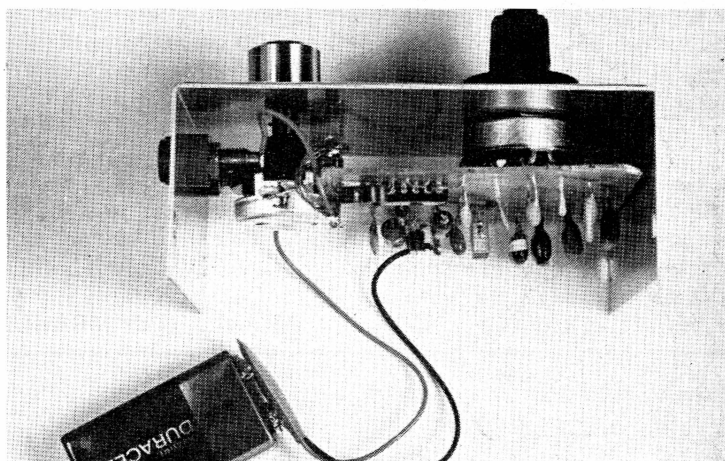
Le module est maintenu sous le couvercle du boîtier métallique uniquement par le serrage de l'écran du rotacteur.
